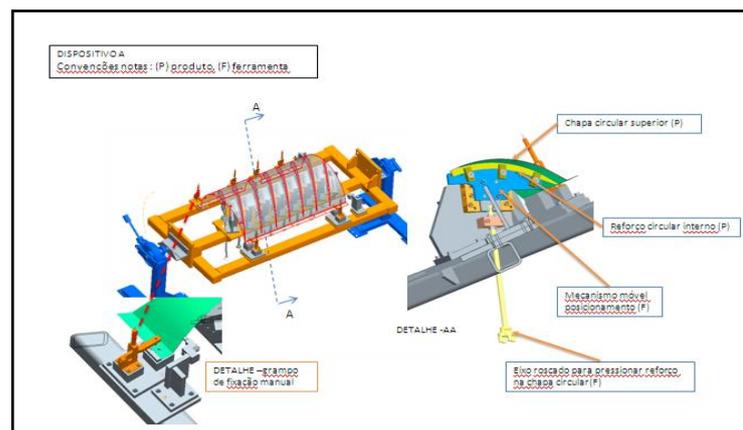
Dispositivo de solda A. Fonte: Pesquisa (2012)
